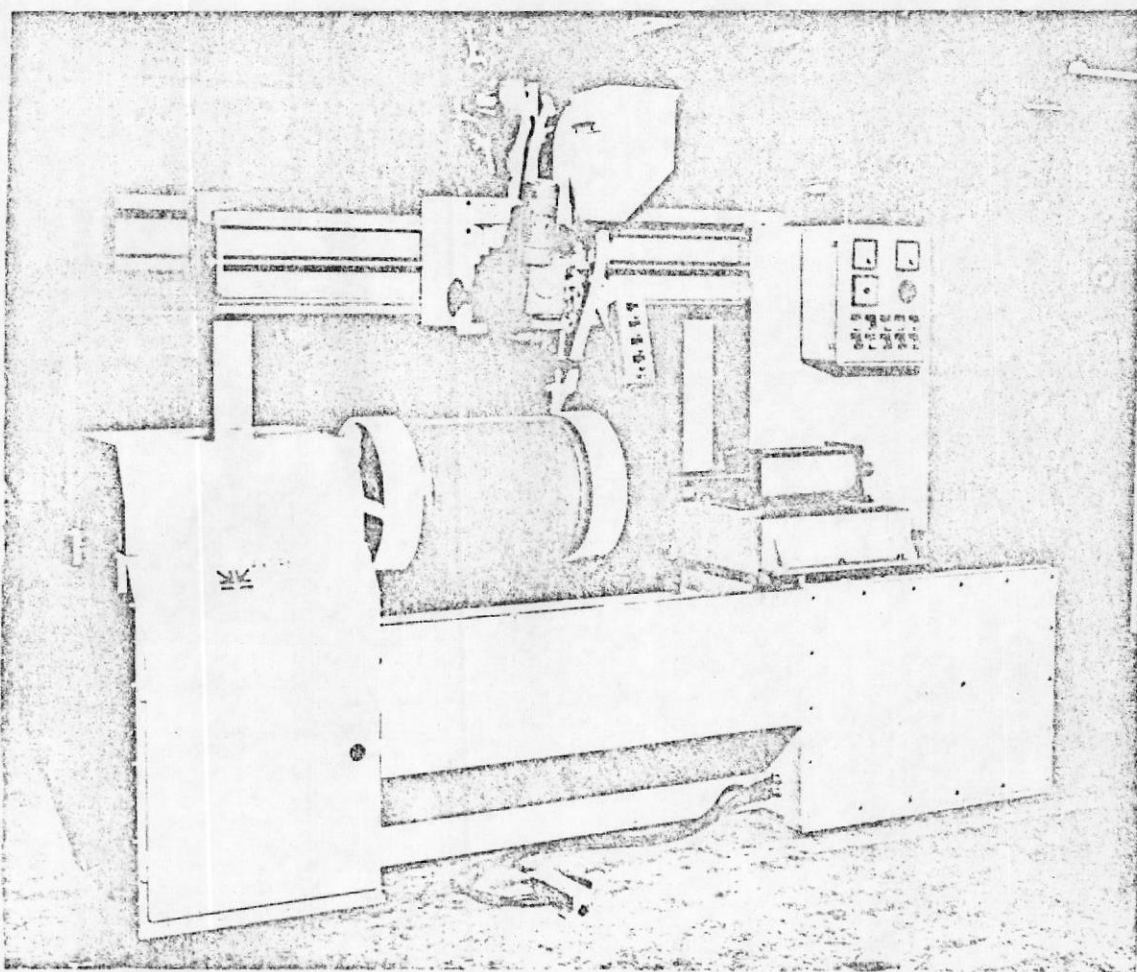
MAQUINA DE SOLDAR POR ARCO SUMERGIDO
